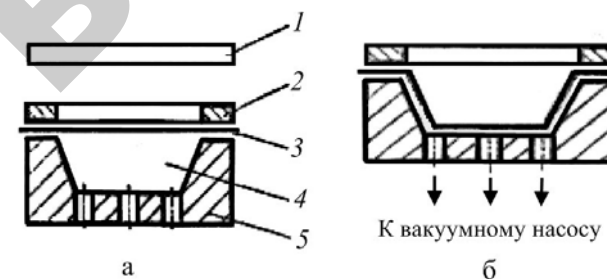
Схема вакуумного формования: а — нагрев; б — формование; 1 — нагреватель; 2 — прижимная рамка; 3 — лист термопласта; 4 — вакуумная камера; 5 — форма
